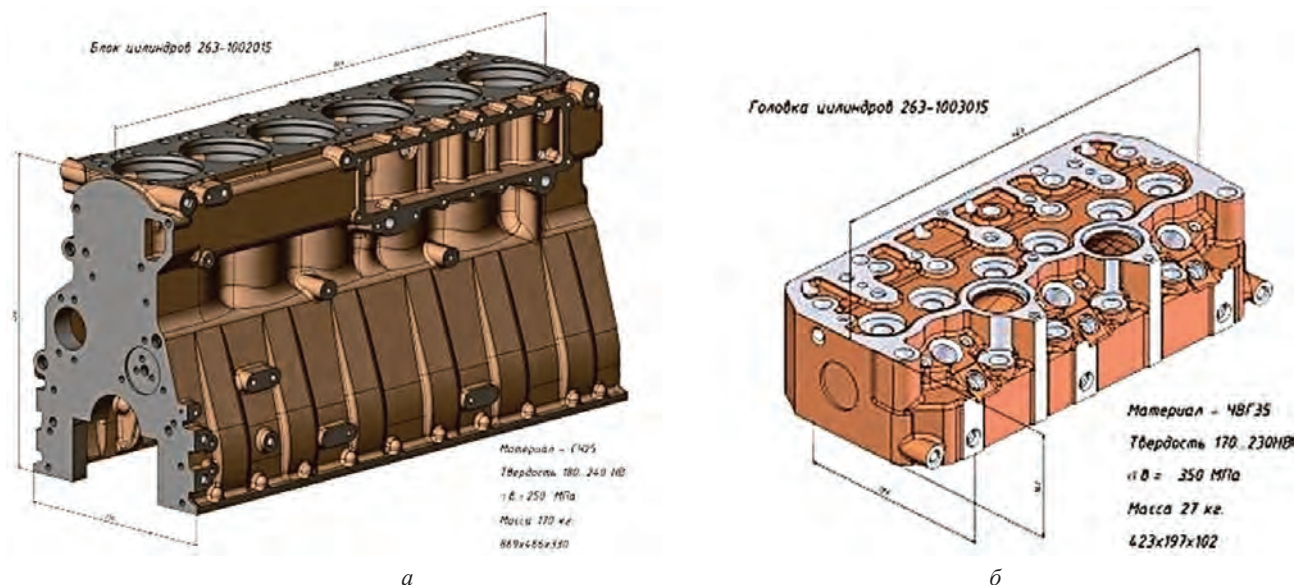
Примеры сложнопрофильных отливок из железоуглеродистых сплавов: а – блок цилиндров; б – головка блока цилиндров
